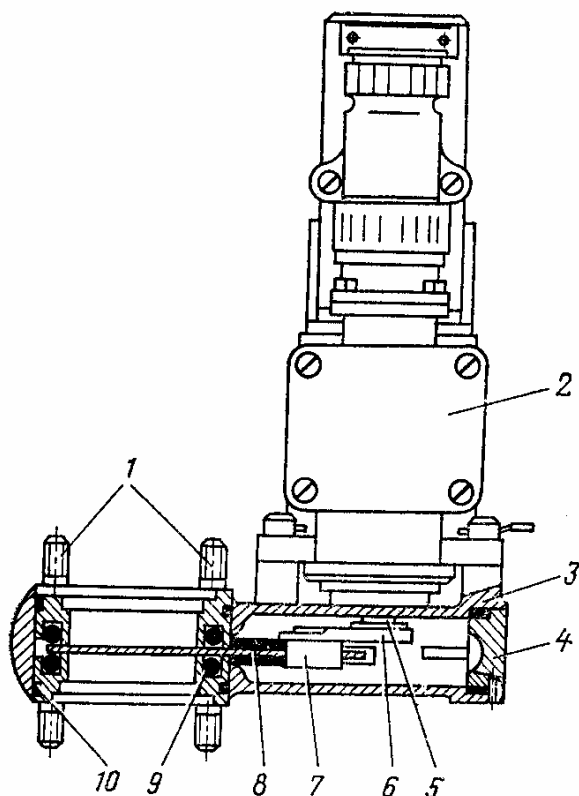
Перекрывной (пожарный) кран 768600МА:
